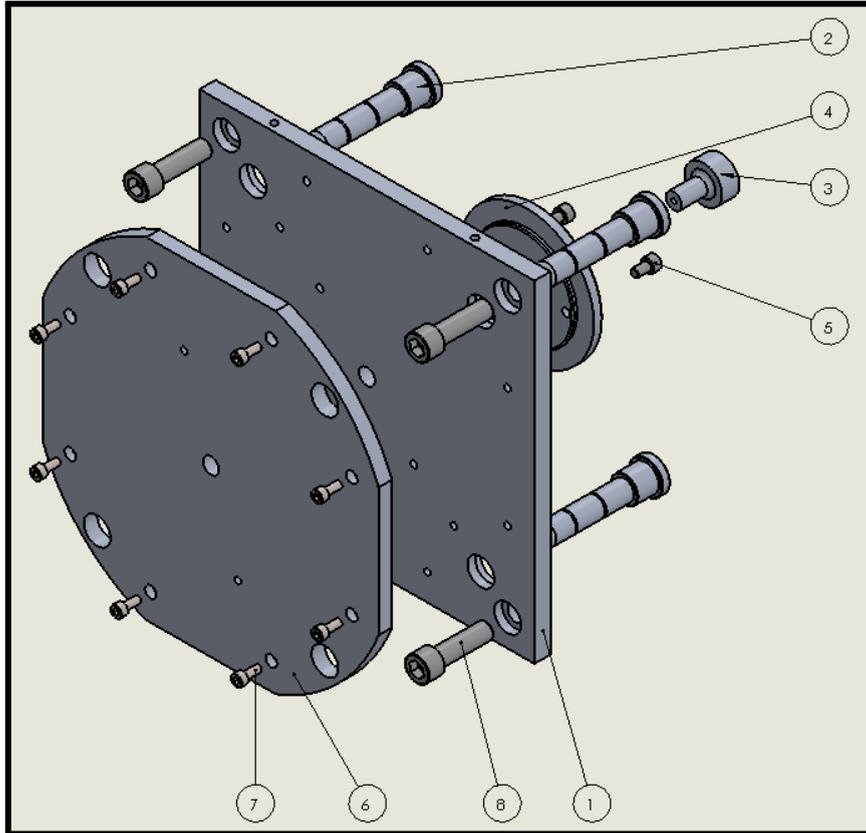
M. Vista explosionada de la configuración básica de la parte fija del portamolde
